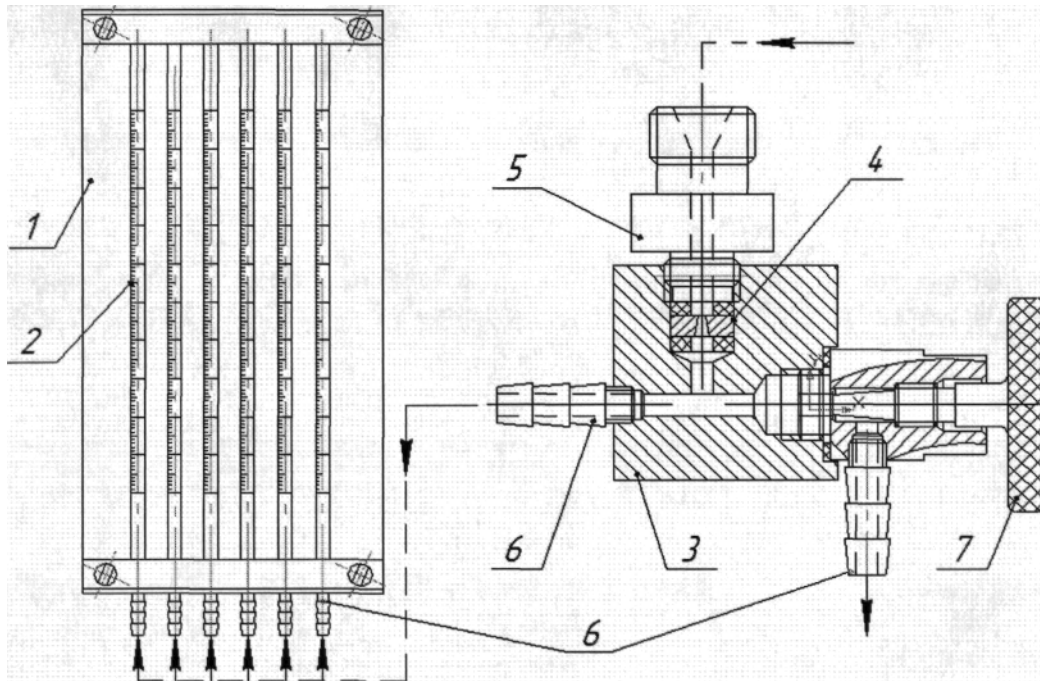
Загальний вигляд пристрою циклічної подачі палива: 1 — блок мензурки; 2 – об'ємні колби (мензурки); 3 – корпус імітатора форсунки; 4 – вбудований калібрований жиклер; 5, 6 – технологічні плунжери для підключення паливопроводів; 7 – дросельні заслінки.
